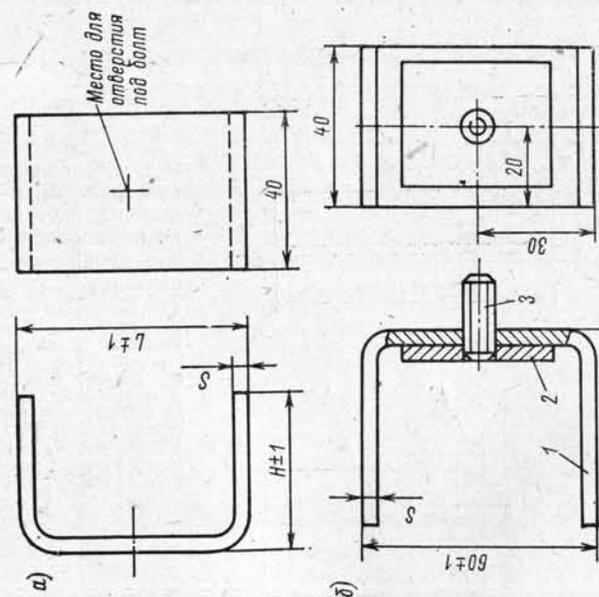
Мосты приварные для крепления электрооборудования: *а* — для помещений без зашивки изоляции; *б* — для помещений с зашивкой изоляции.
